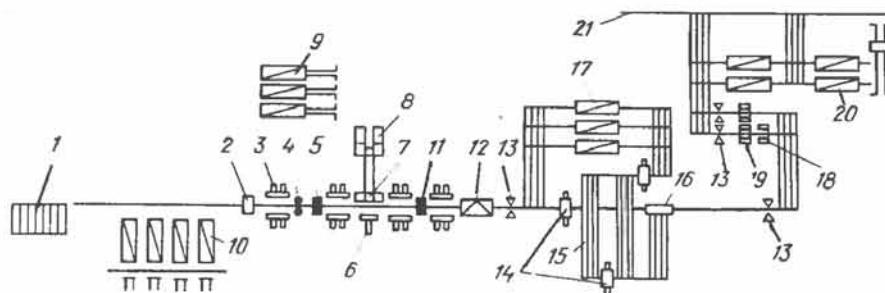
Схема расположения оборудования толстолистового стана 3600:
